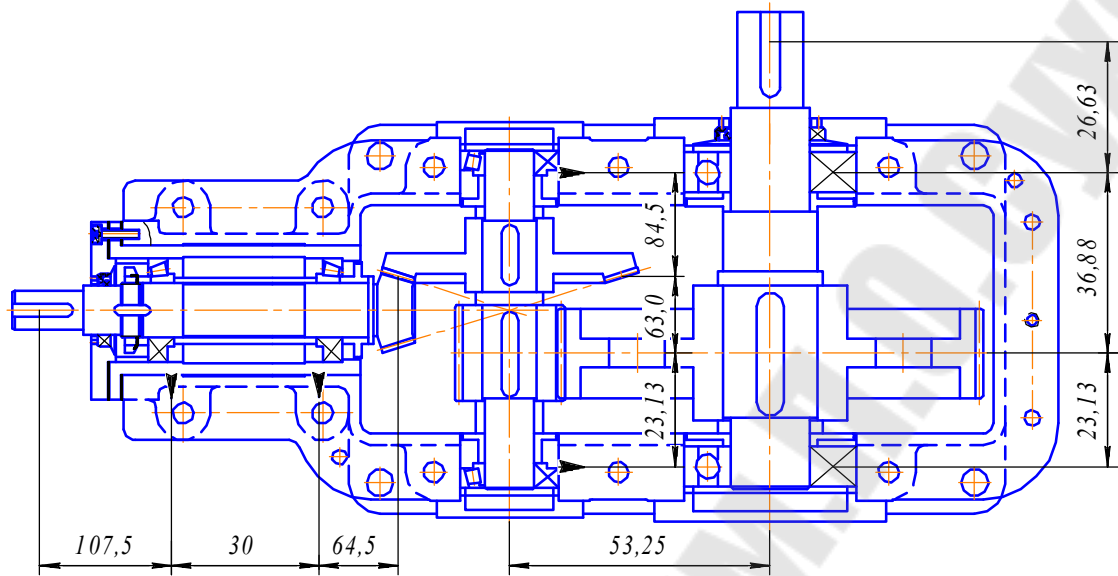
Рис. III. Компонировочная схема двухступенчатого коническо-цилиндрического редуктора
